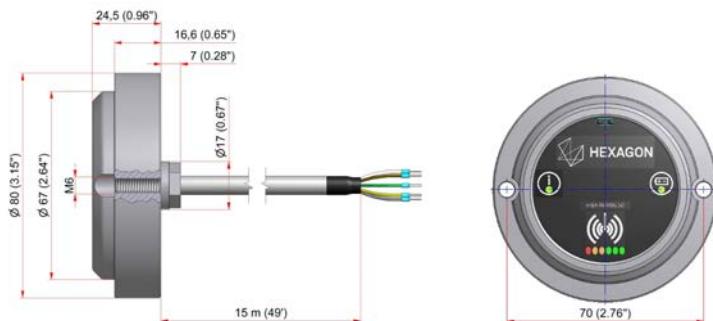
Dimensiones RWR95.50-A (salida de cable axial)
